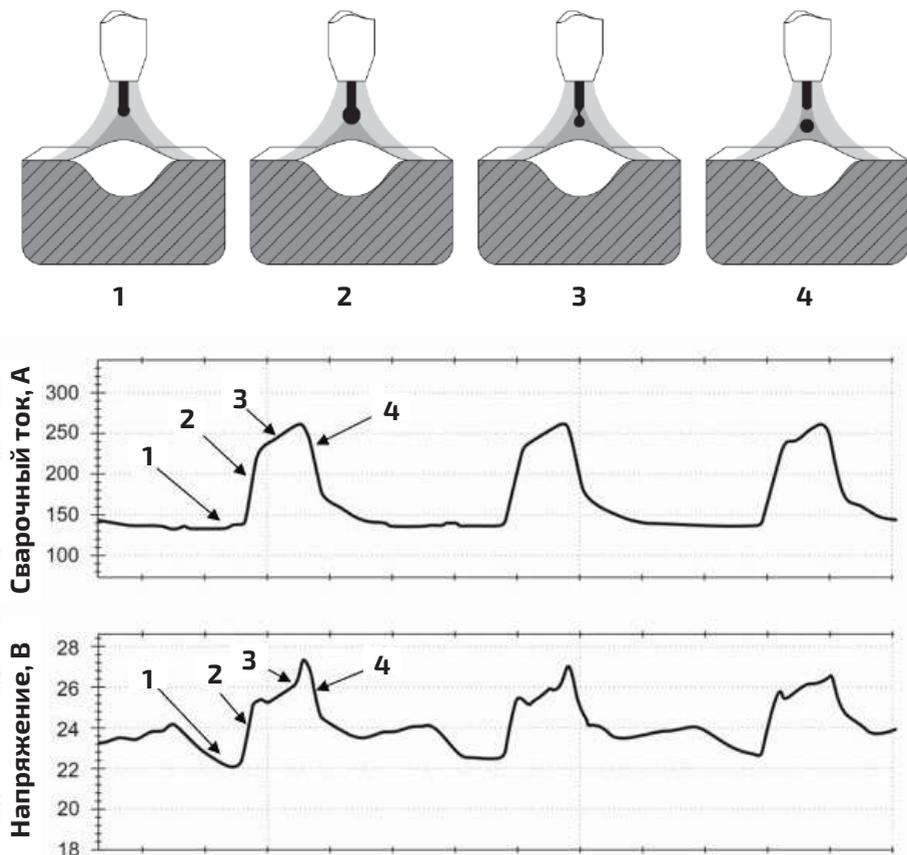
Перенос металла проволоки в сварочную ванну.
